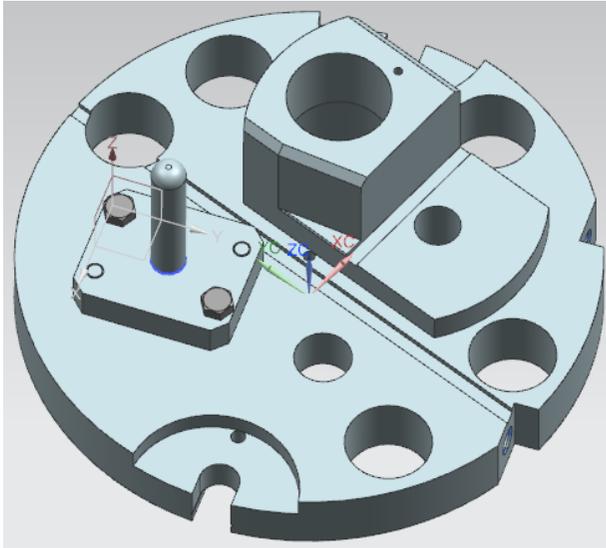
Окончательный вид деталей «Штифт_1» в сборке
